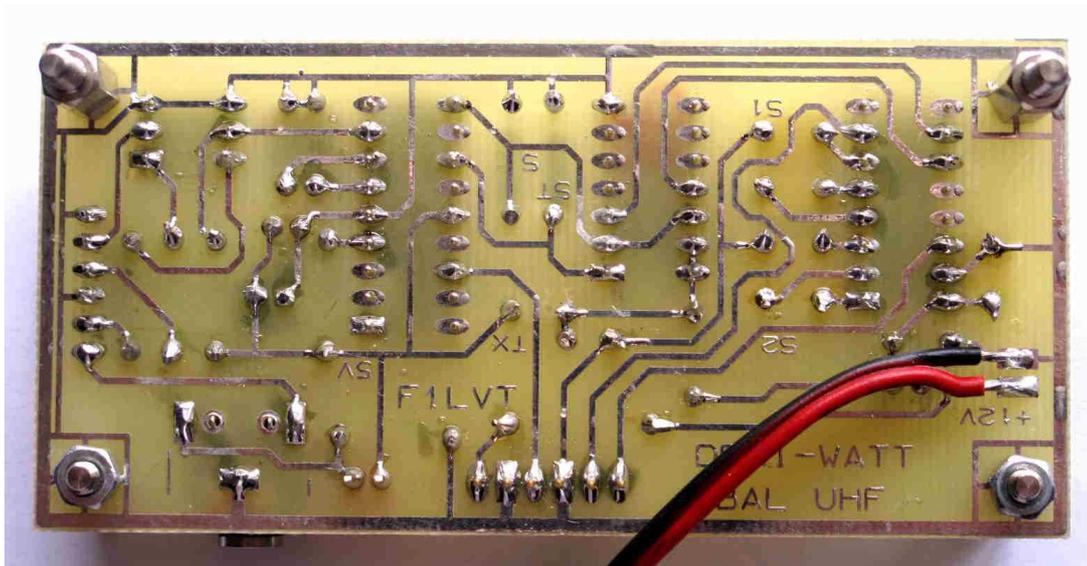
Carte de pilotage de la balise « Quart de Watt » vue côté soudures
